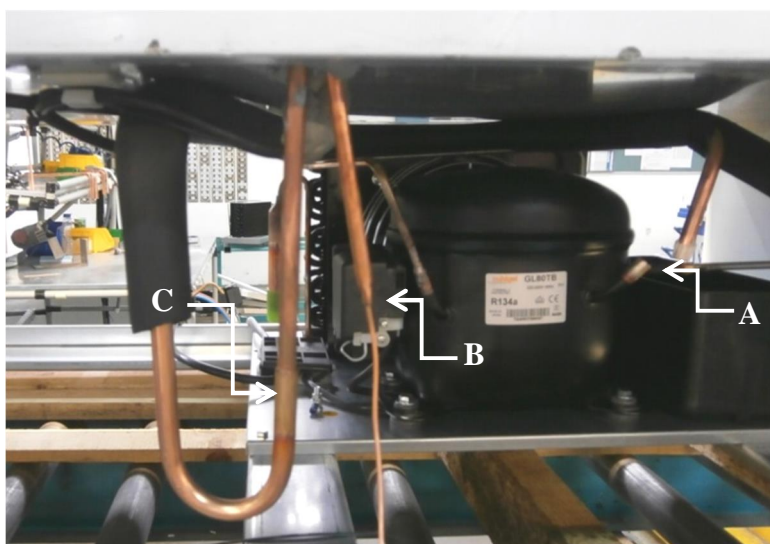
Operações de soldadura com o grupo de frio montado na bancada
